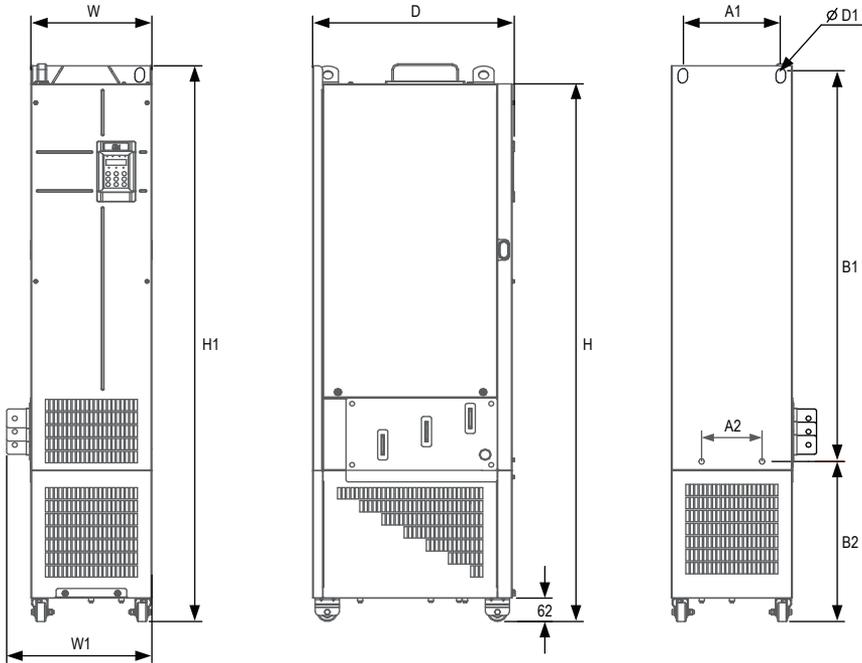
CE300-4T220 ~ CE300-4T400 外型尺寸及安装尺寸示意图
